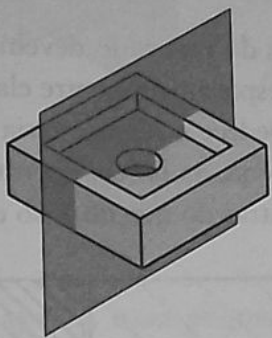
Plano de corte que passa por plano de simetria da peça.
